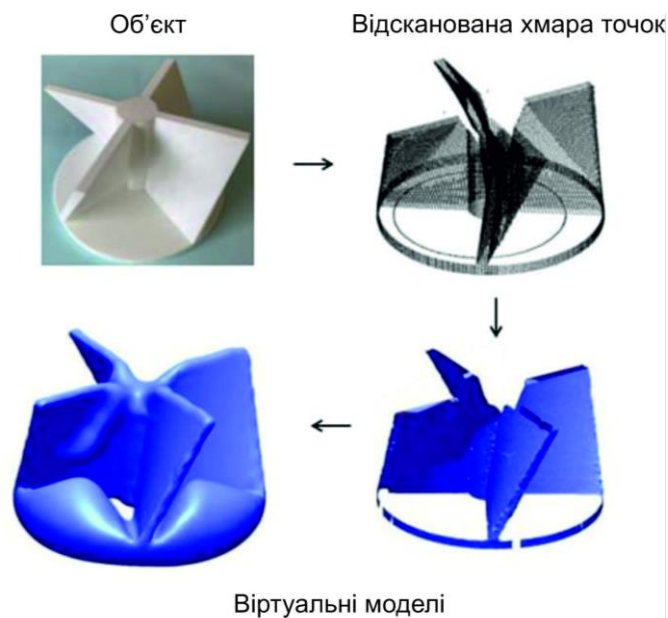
Схема звичайного реверс-інжинірингу
